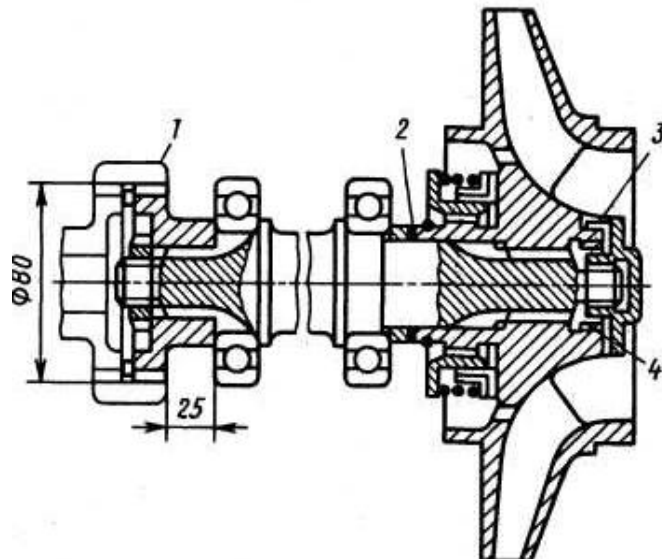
Схема валу в зборі з підшипниками, крильчаткою і приводним фланцем
